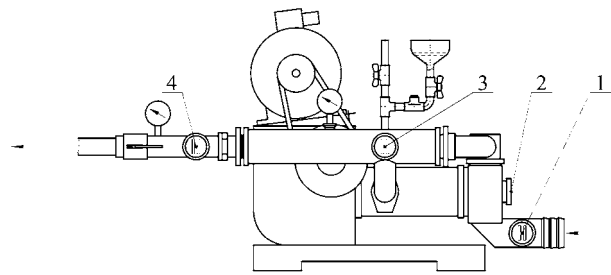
Схема встановлення тензометричних датчиків: 1 – усмоктувальний патрубок; 2 – усмоктувальна робоча камера; 3 – робоча камера компенсатора; 4 – нагнітальний патрубок
